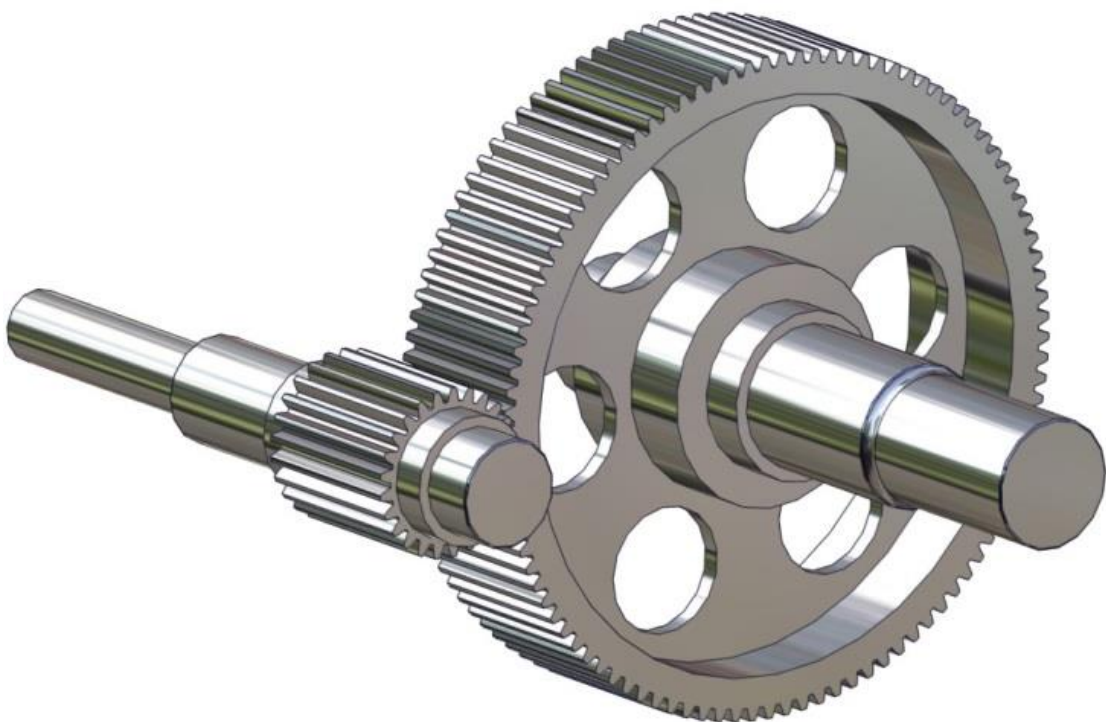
3D-модель цилиндрической зубчатой передачи внешнего зацепления
